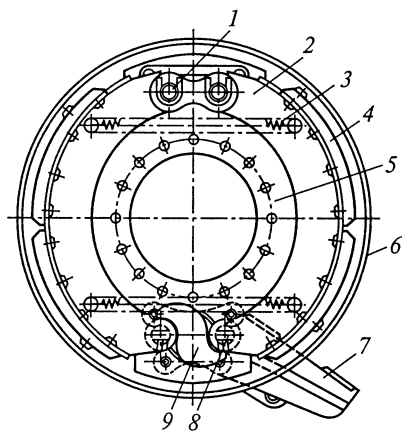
Колесный тормозной механизм грузовых автомобилей КамАЗ:
